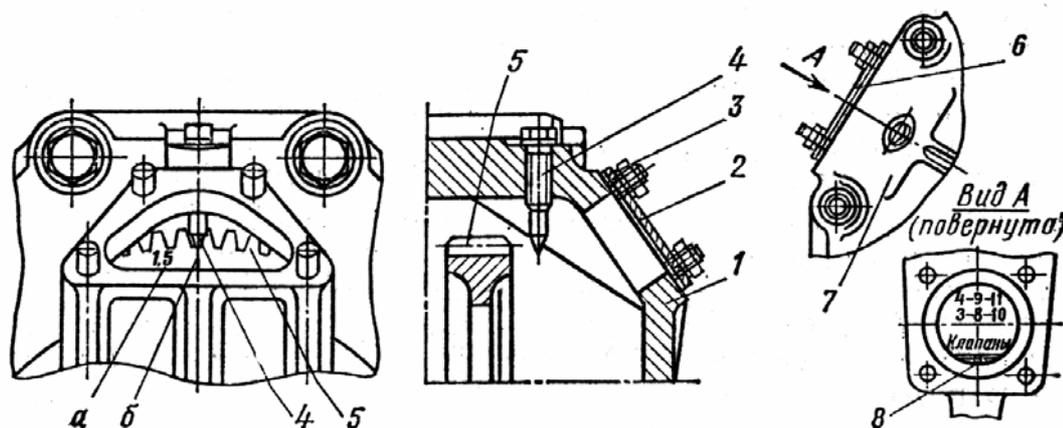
Вид на метки для регулировки клапанного механизма двигателя ЯМЗ-240Б:
